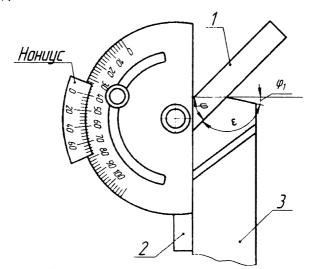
Схема измерения угла φ токарного проходного резца
